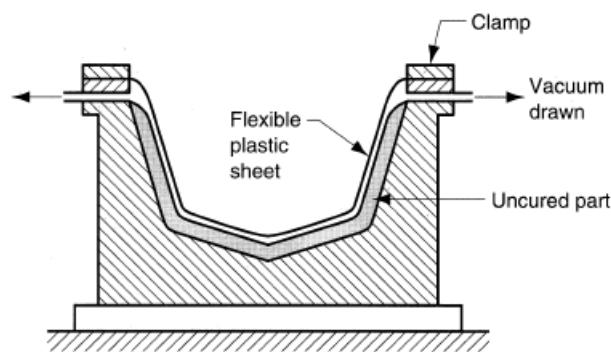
Stampaggio sottovuoto (Vacuum bag moulding)
